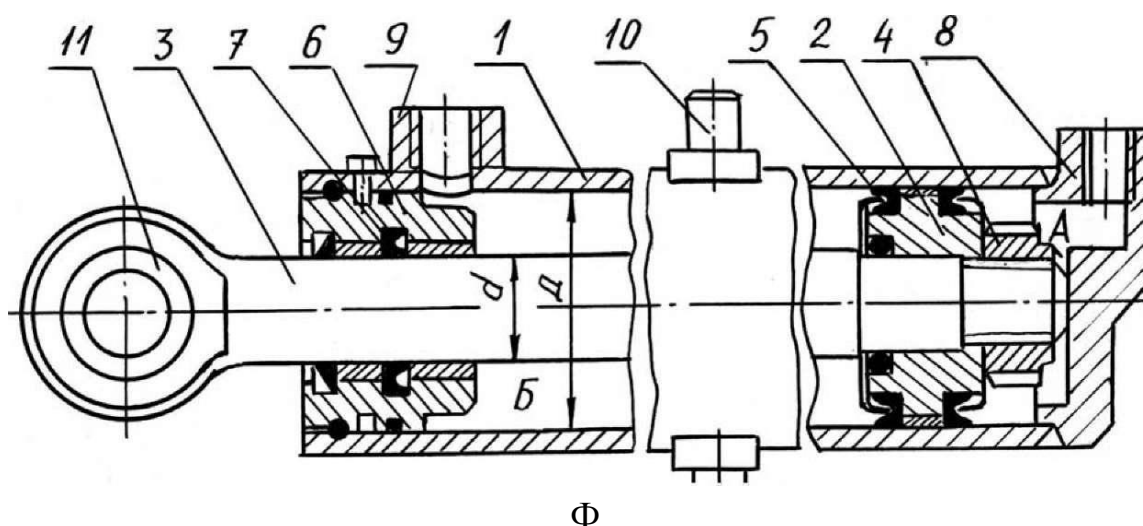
Гидроцилиндр бульдозера ДЗ-42
